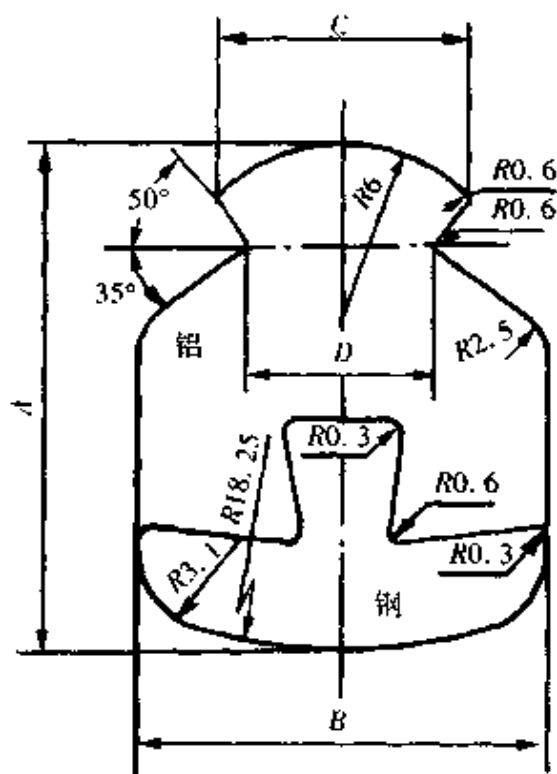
GLCB 型钢铝电车线截面尺寸
